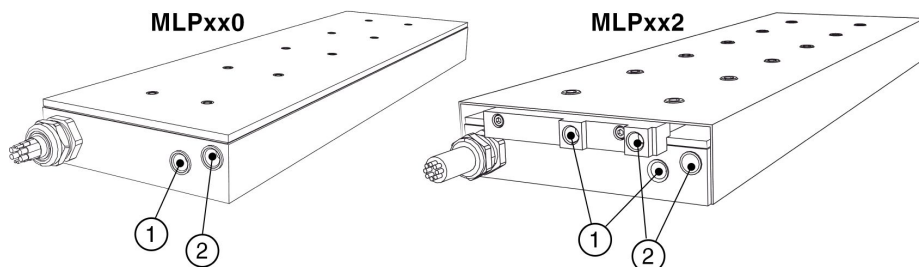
Coppie di serraggio nominali per le viti di fissaggio delle parti primarie
